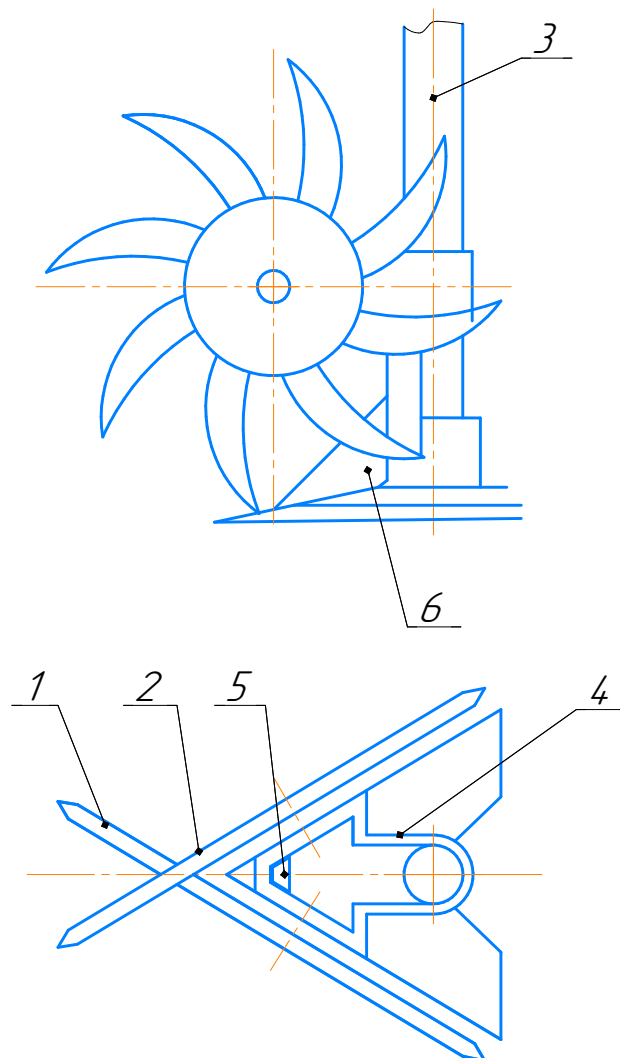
Схема запропонованої конструкції сошника де 1 і 2 – голчасті диски; 3 -стійка сошника; 4 -вилка; 5 -шарнірна ланка; 6 - лобова поверхня.
